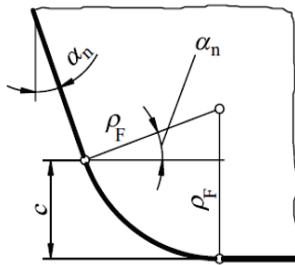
Kremayerle diş dibi geometrisinin kesilişi [4] (Gear tooth fillet generation by the rack cutter (Gear Hob))
